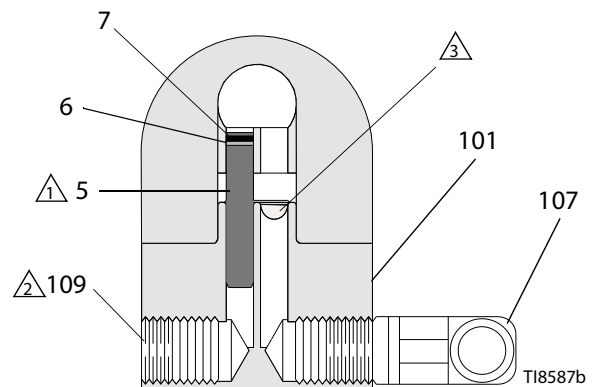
Показана установка без циркуляции (вид в разрезе)
